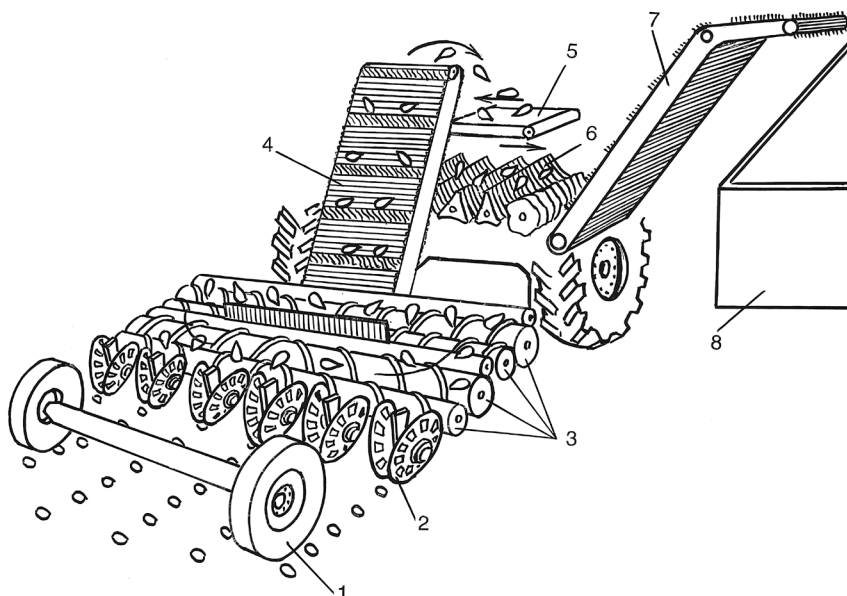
Схема корнеуборочной машины: 1 – направляющие колеса; 2 – выкапывающий аппарат; 3 – шнековый очиститель; 4 – продольный транспортер; 5 – поперечный ленточный транспортер; 6 – комкодробитель; 7 – выгрузной транспортер; 8 – транспортное средство
